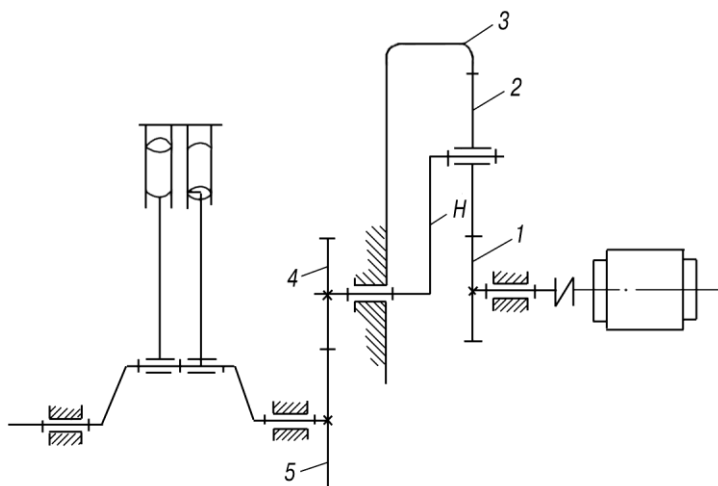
Механизм зубчатой передачи воздушного компрессора
